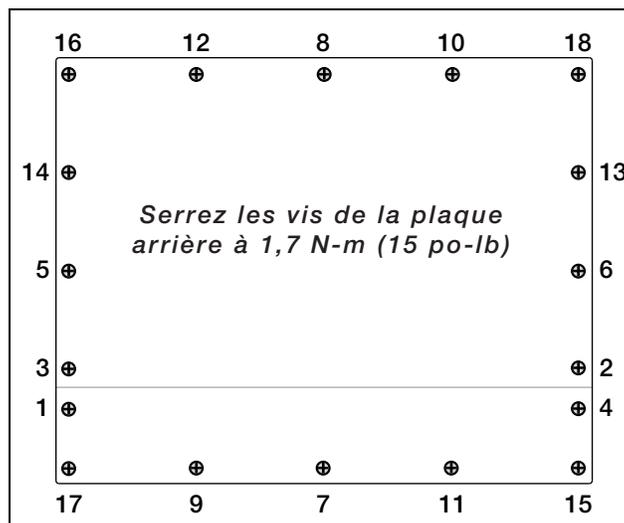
820i Plaque arrière de boîtier pour indicateurs et 920i.
